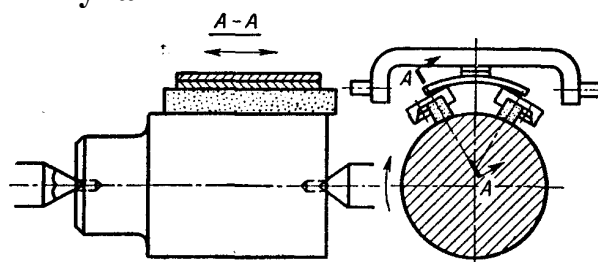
Схема обробки зовнішньої поверхні
